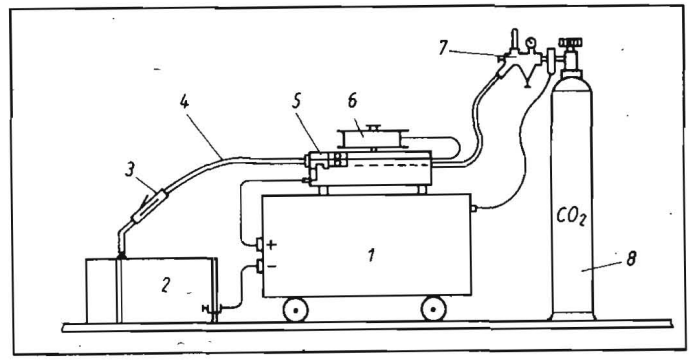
Aufbau eines Schweißplatzes zum MAG-Hand-Schweißen;
